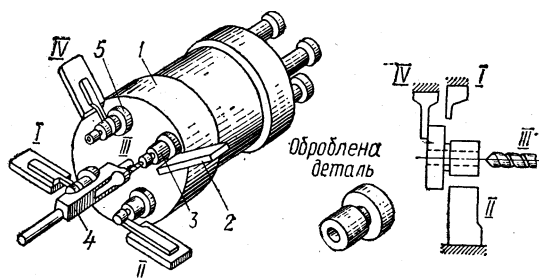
Схеми обробки на багатошпindelному токарному автоматі послідовної дії
